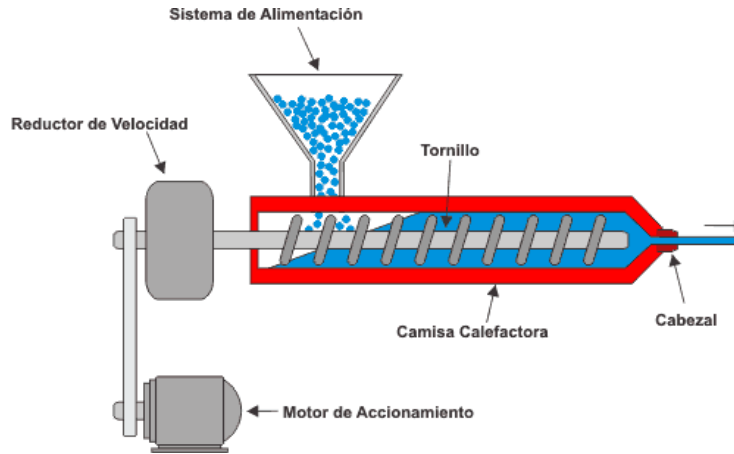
Esquema de moldeo por extrusión. Fuente: 51
